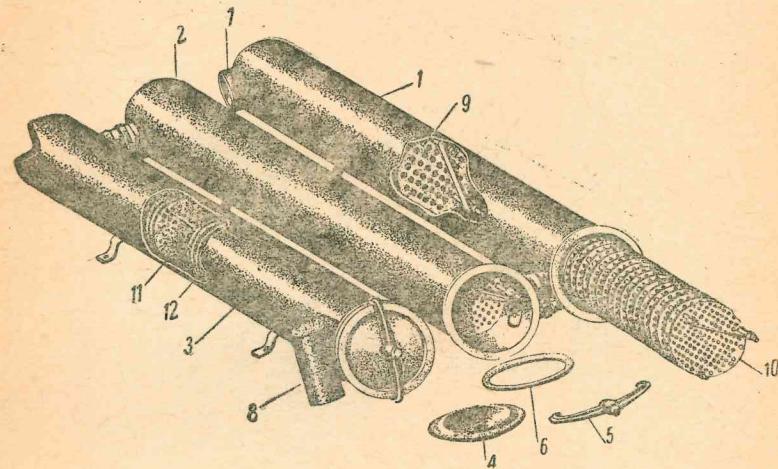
Устройство батареи грубых очистителей-охладителей газа установки ЗИС-21 (для наглядности часть наружных корпусов вырезана):
